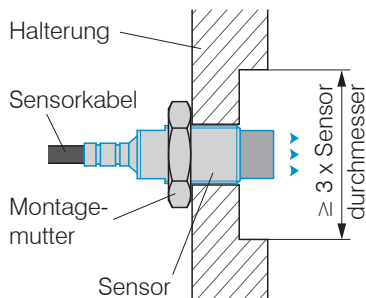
Flächenbündige Montage eines ungeschirmten Sensors in einer metallischen Halterung mit Aussparung
